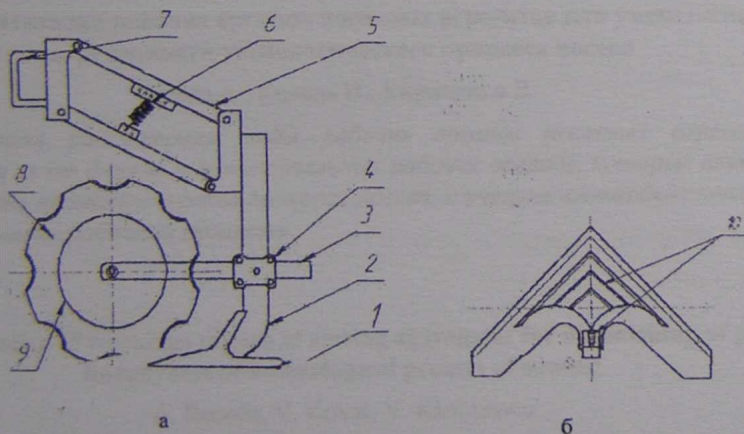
Універсальний робочий орган: а - загальний вид; б – робоча лапа з розподільчим механізмом; 1- стрілочата лапа; 2 – пола стійка та формувач потоку насіння; 3 – стійка дискового ножа; 4 – кріплення стійки дискового ножа; 5 – паралелограмний механізм; 6 – утримуюча пружина; 7 – кріплення УРО до рами посівного агрегату; 8 – дисковий ніж; 9 – реборда дискового ножа, 10 – розподільча система
